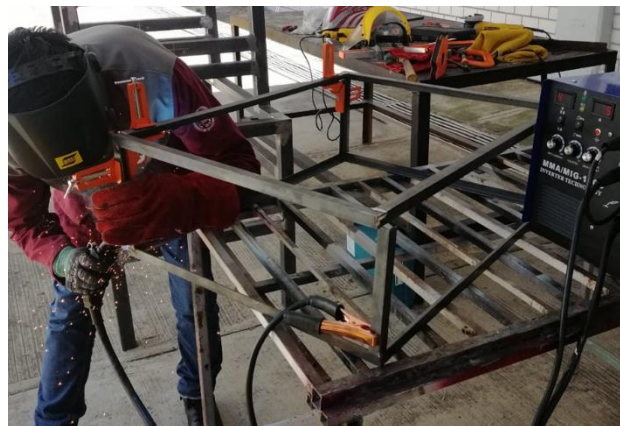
Soldadura de la estructura del cernidor.
